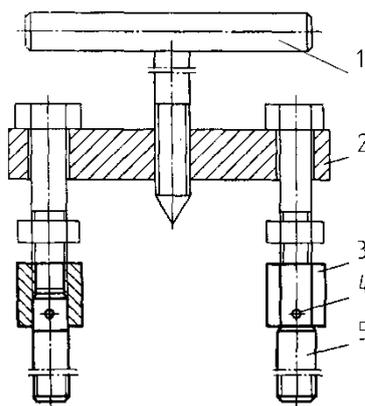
Приспособление для снятия фрез ИП.12.000
